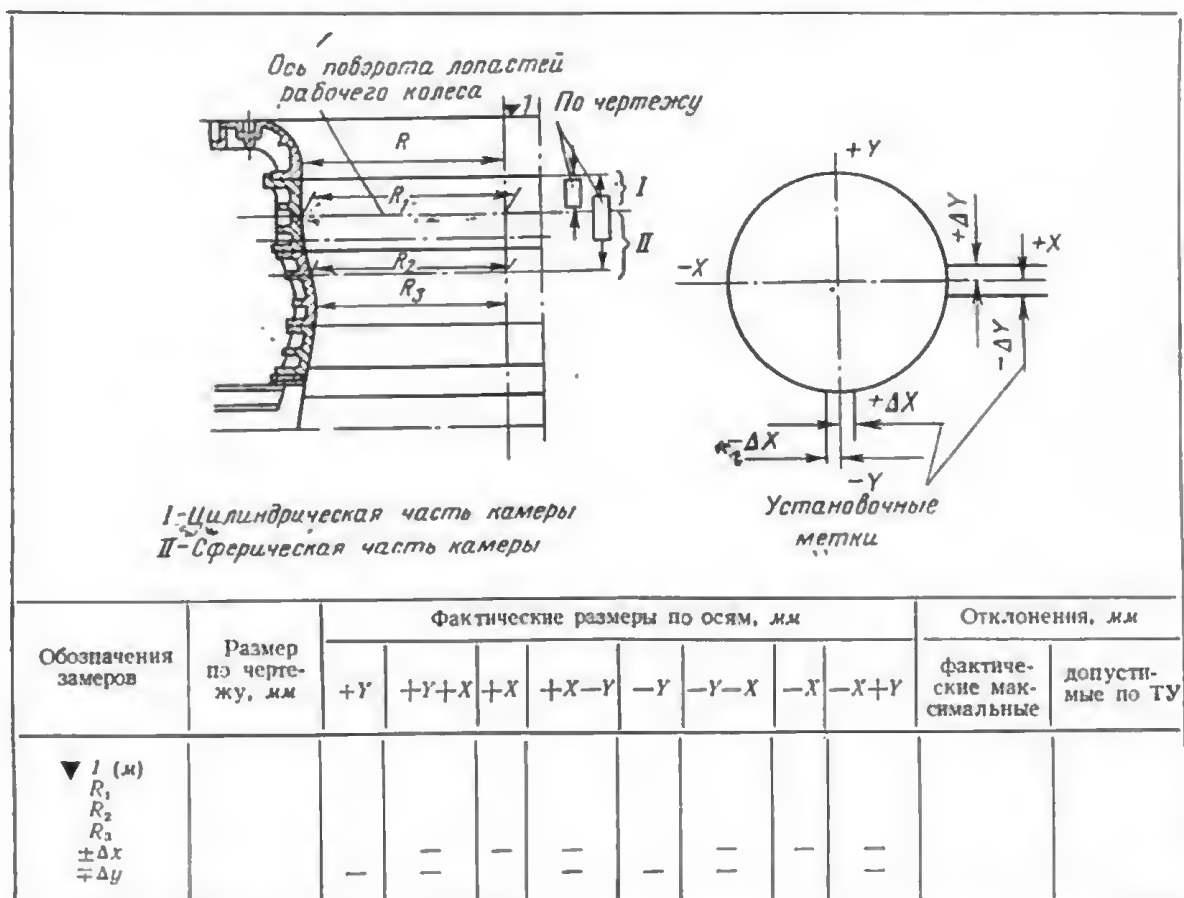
Формуляр установки камеры рабочего колеса и нижнего кольца направляющего аппарата.
